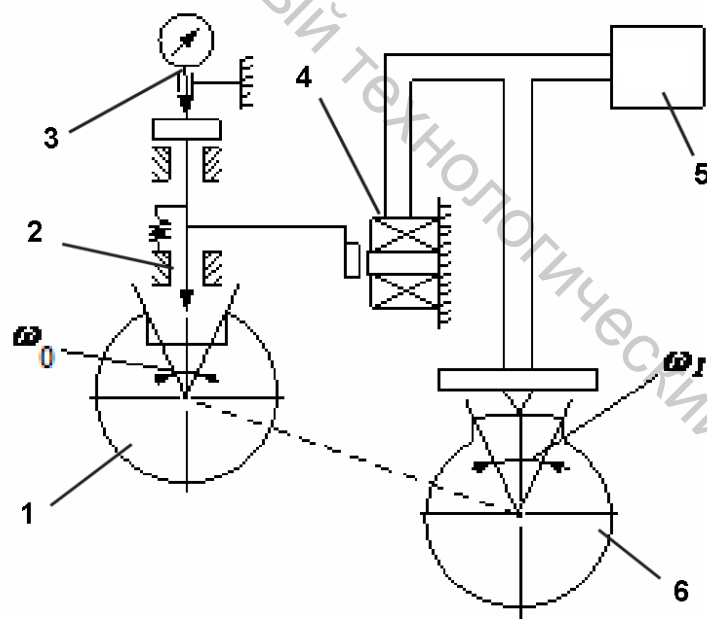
Схема прибора с затормаживанием измерительных наконечников: 1 – обрабатываемая деталь; 2 – измерительный наконечник; 3 – измерительный прибор; 4 – электромагнит; 5 – исполнительный механизм; 6 – кулачок
